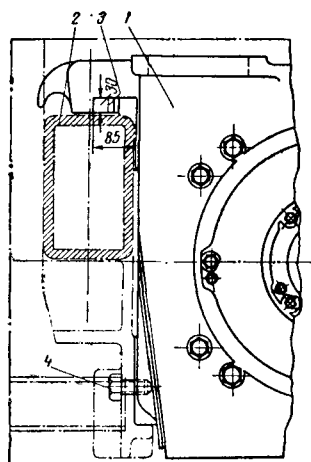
Установка тягового двигателя на съёмной балке: 1 — тяговый двигатель; 2 — съёмная балка
